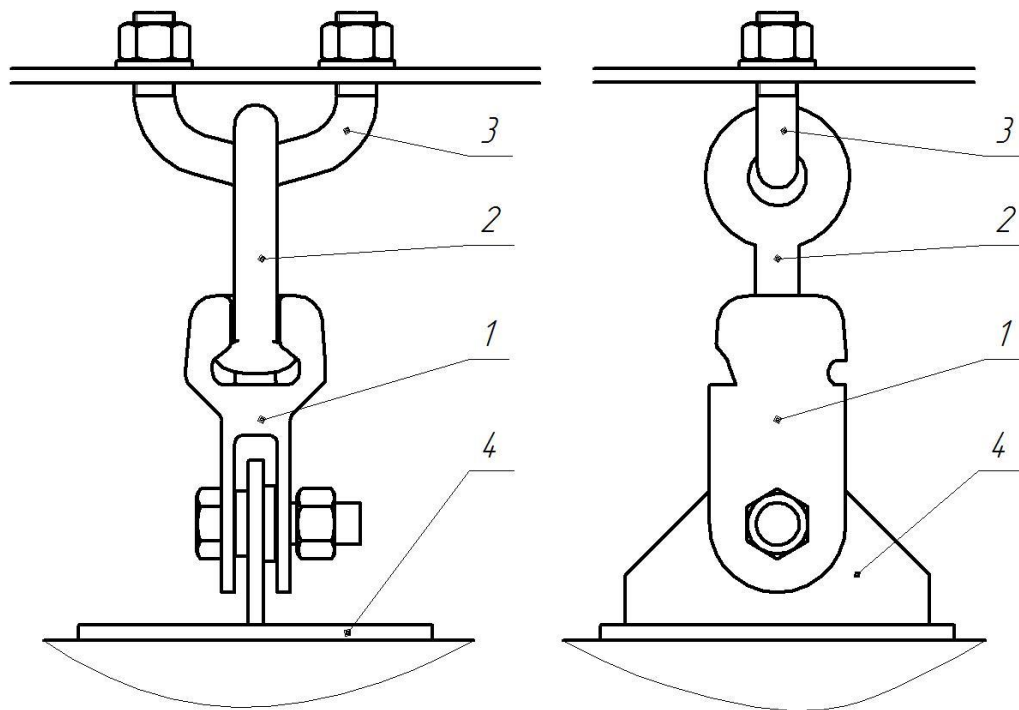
крепление устройства E-TOR-110 на опоре электропередачи или портале.
